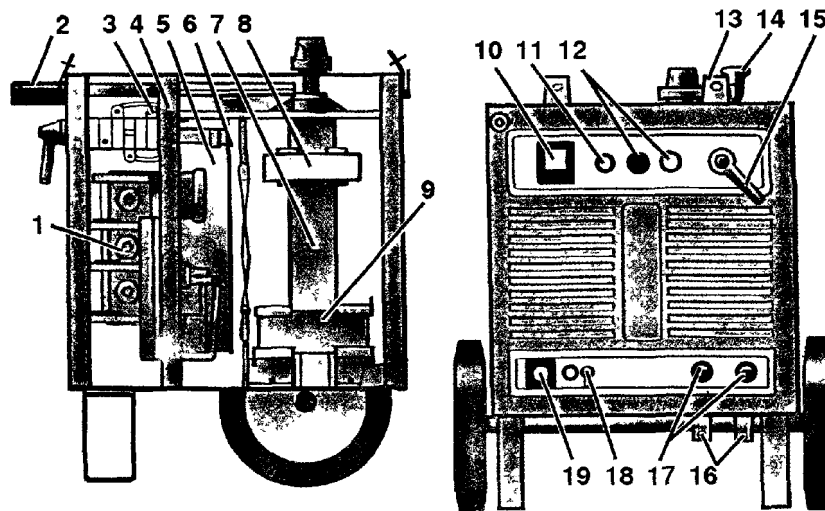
Зварювальний випрямляч: 1 - випрямний блок; 2 - висувні ручки; 3 - запобіжники; 4 - блок апаратів; 5 - вентилятор; 6 - реле; 7 - силовий трансформатор; 8 - вторинна обмотка; 9 - первинна обмотка; 10 - амперметр; 11 - лампа; 12 - кнопки вимикача; 13 - скоби; 14 - рукоятка регулювання струму; 15 - перемикач діапазонів струму; 16 - шини зворотного заземлення; 17 - струмові рознімачі; 18 - болт заземлення; 19 – штепсельний рознімач для підключення до мережі
